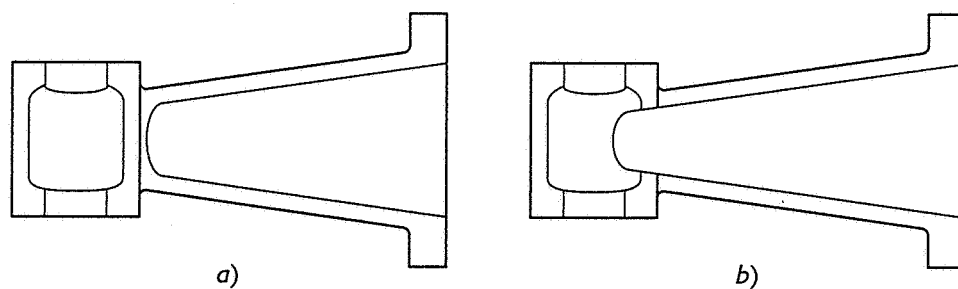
Disegno scorretto a) e corretto b) di una parte di un getto.
